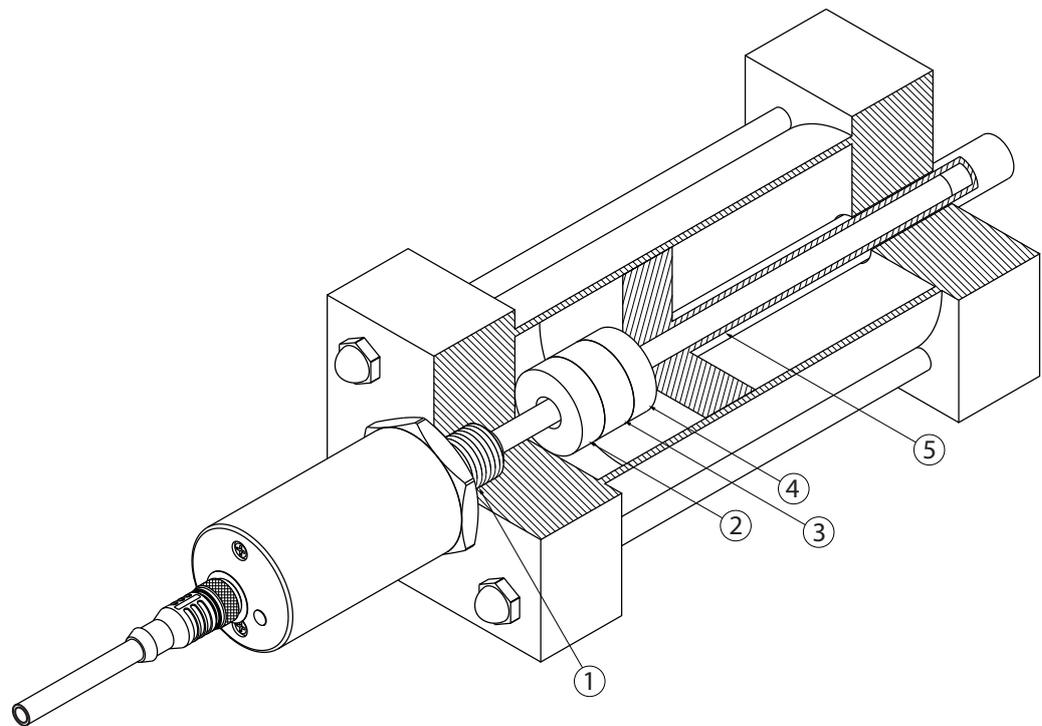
Gerät in einen Hydraulikzylinder montieren
